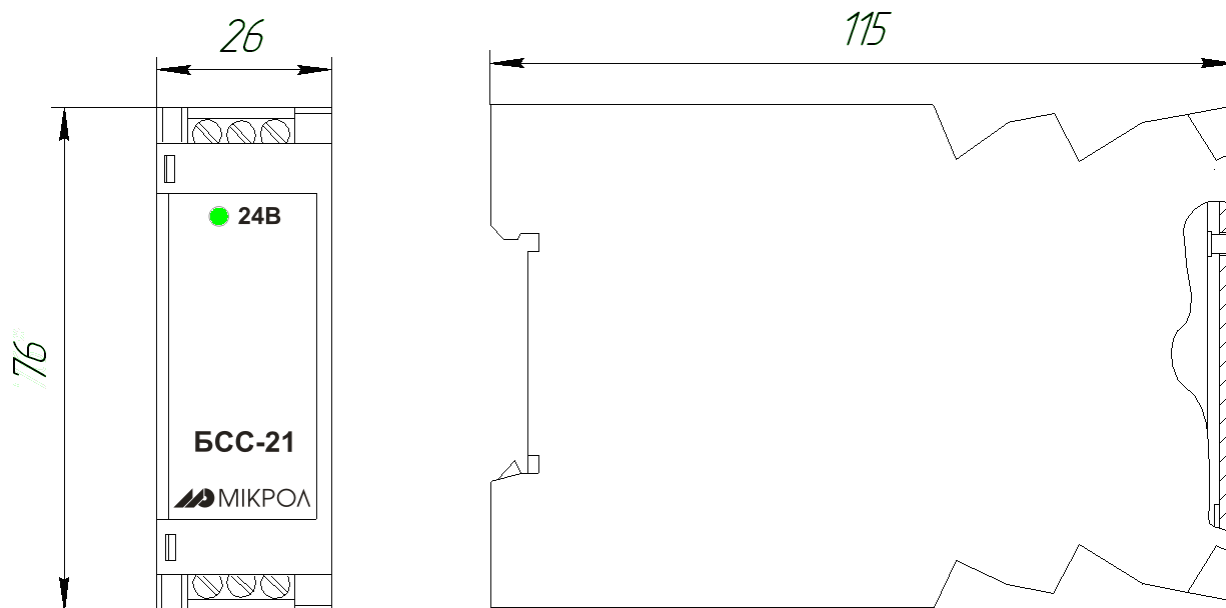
Зовнішній вигляд та габаритні розміри БСС-21
